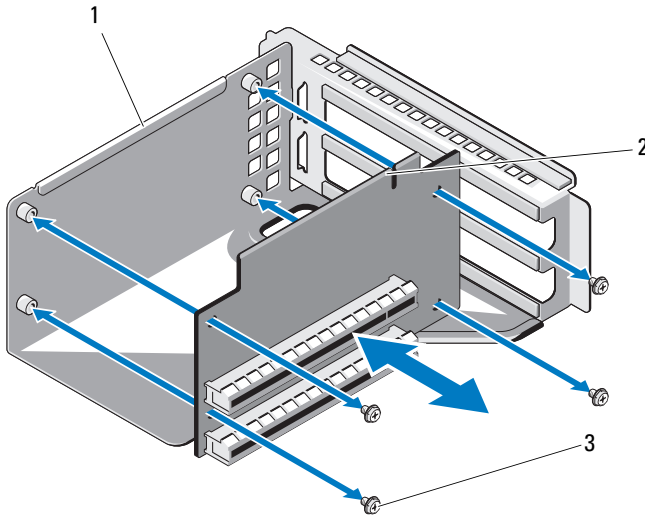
Retrait et installation du module de carte de montage pour carte d'extension
